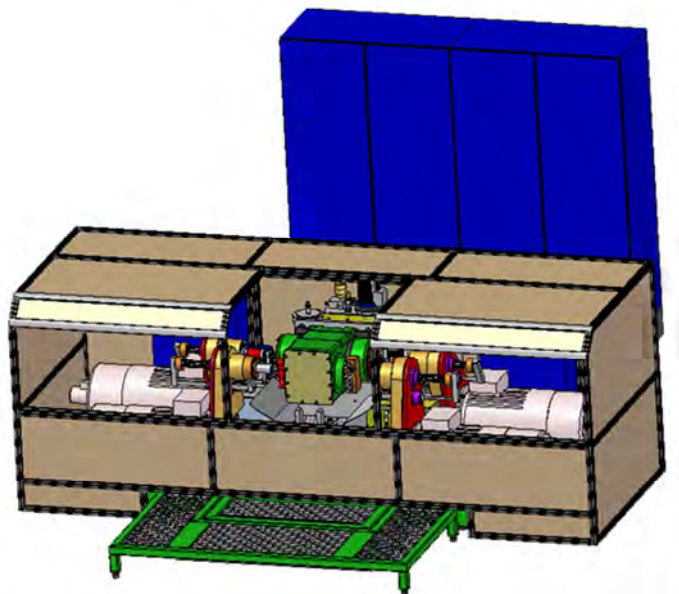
L BANCO DE PRUEBAS DE RODADURA
